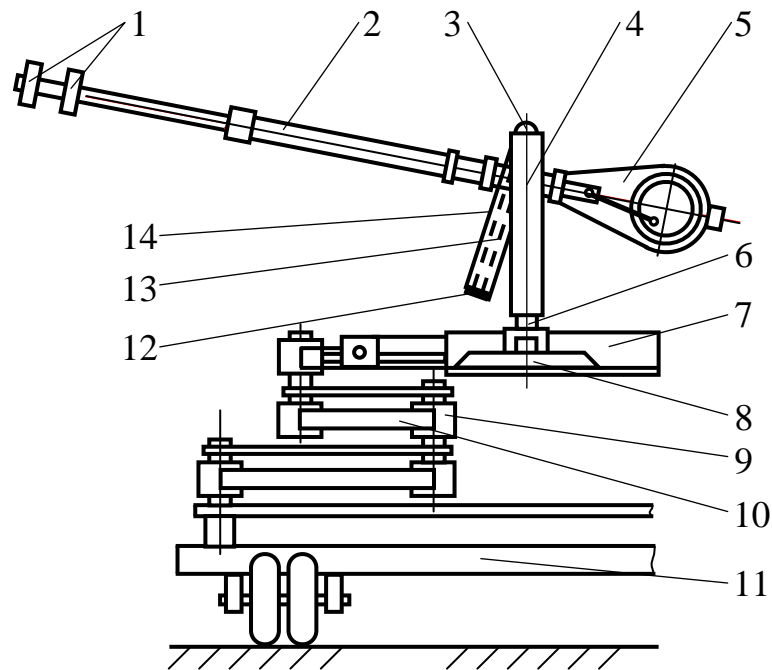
Схема турельного струшувача плодів (США): 1 – захват; 2 – стріла; 3 – шарнір; 4 – колона; 5 – інерційний кривошипно-повзунний збурювач коливань; 6 – гідроциліндр; 7 – радіально рухома площадка; 8 – поворотна плита; 9, 10 – шарнірно-важільний механізм; 11 – шасі; 12, 13, 14 – пружні П-подібні рамки
